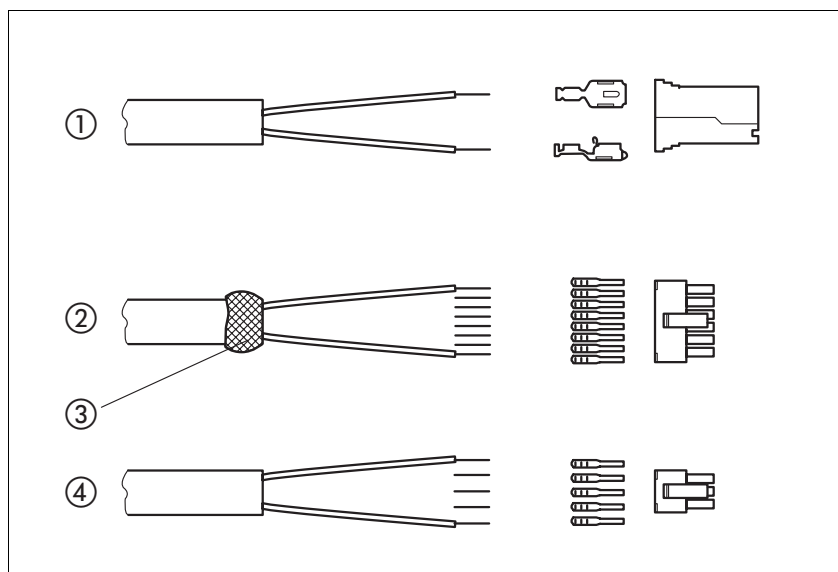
Stecker, Kabelschuhe und Crimpkontakte
